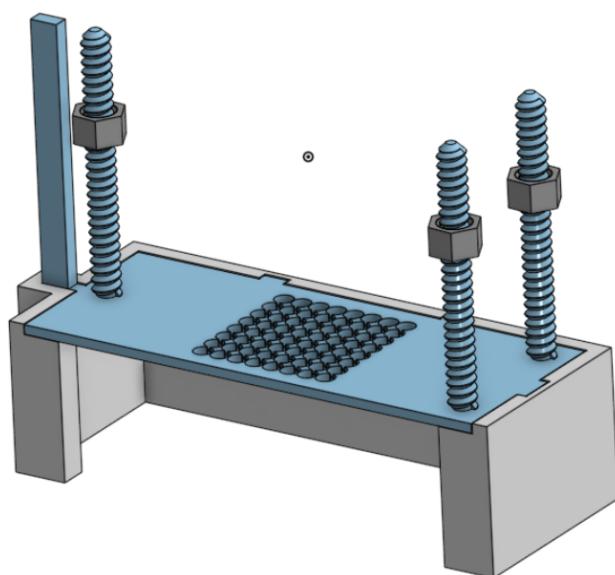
Conception de la partie basse assemblée - Onshape
